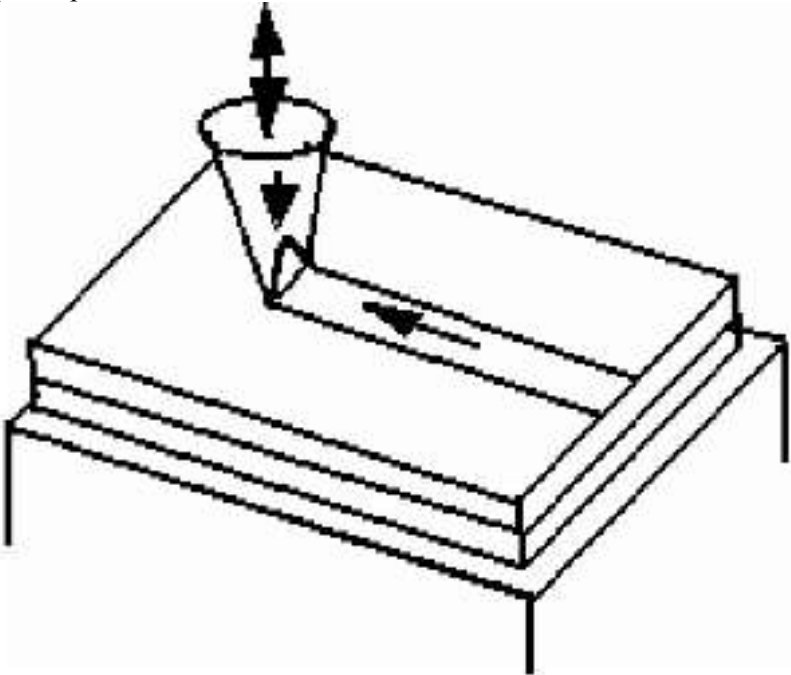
Схема процесу шовного ультразвукового зварювання
